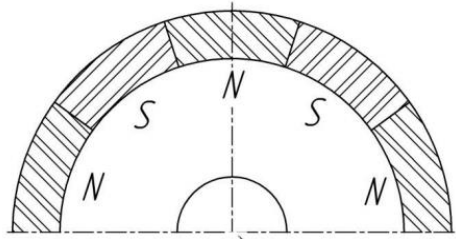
Конструкция ротора с поверхностным расположением магнитов
